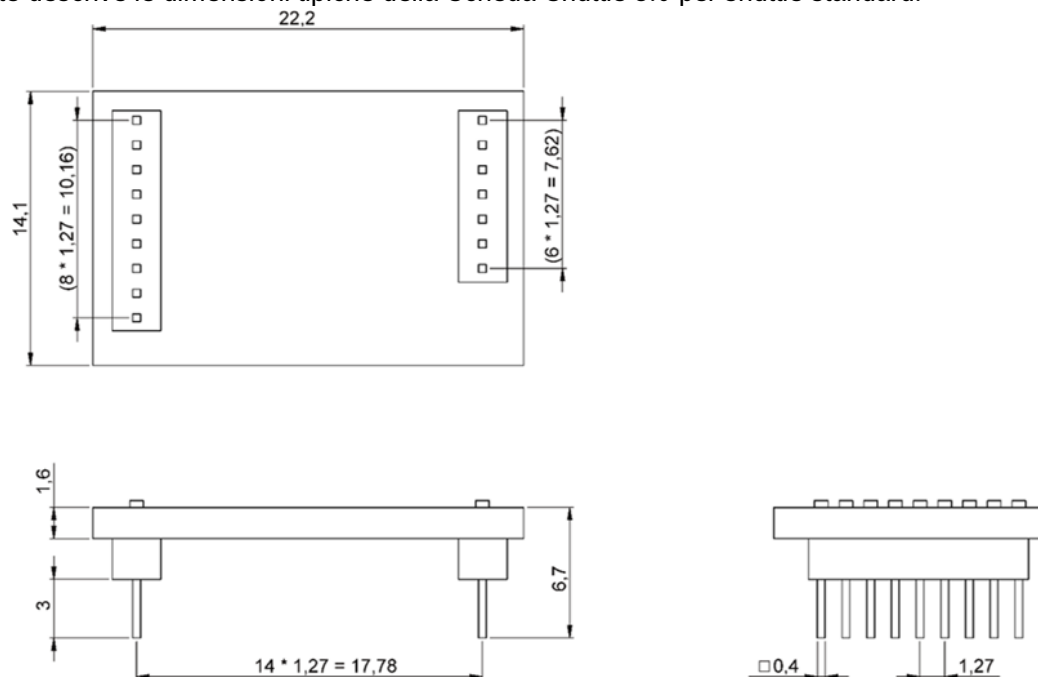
Dimensioni Scheda Shuttle 3.0 standard
